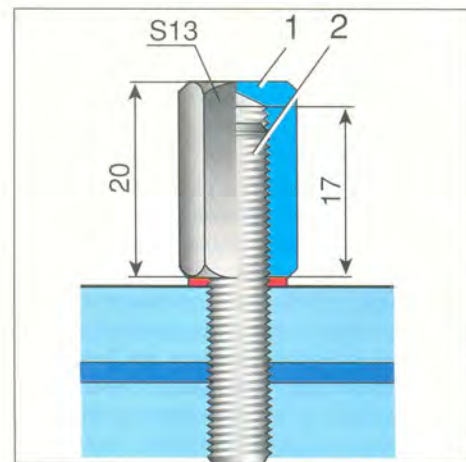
Колпачковая гайка 1 на шпильке 2 коллектора.
